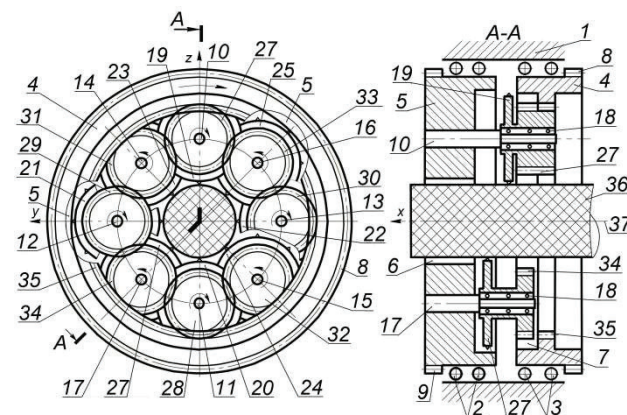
Пристрій для безцентрової обробки циліндричних виробів із ПКМ
